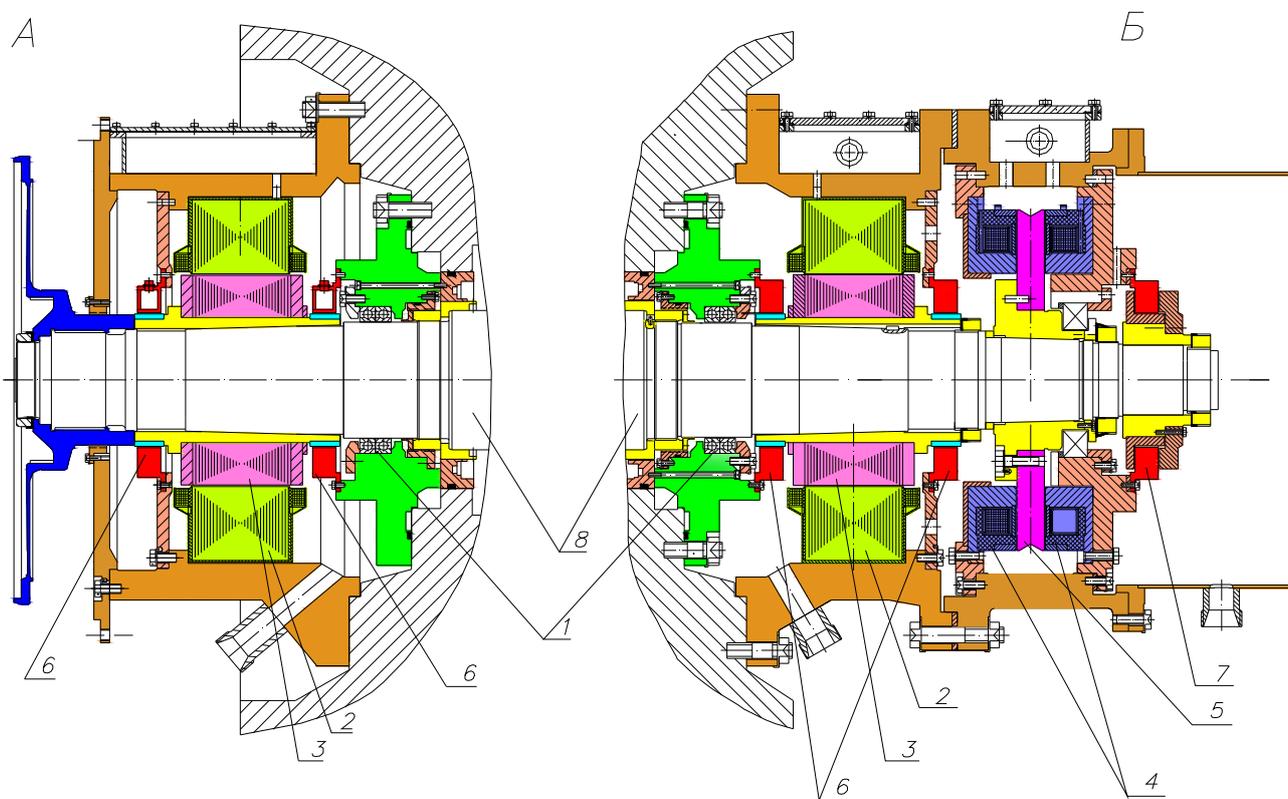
Компоновка ЭМП в компрессоре ГПА: А – со стороны привода, Б – со свободной стороны; 1 – страховочные подшипники; 2 – статор РМП; 3 – ротор РМП; 4 – электромагниты ОМП; 5 – диск ОМП; 6 – блок радиальных датчиков; 7 – блок осевых датчиков; 8 – вал ротора
